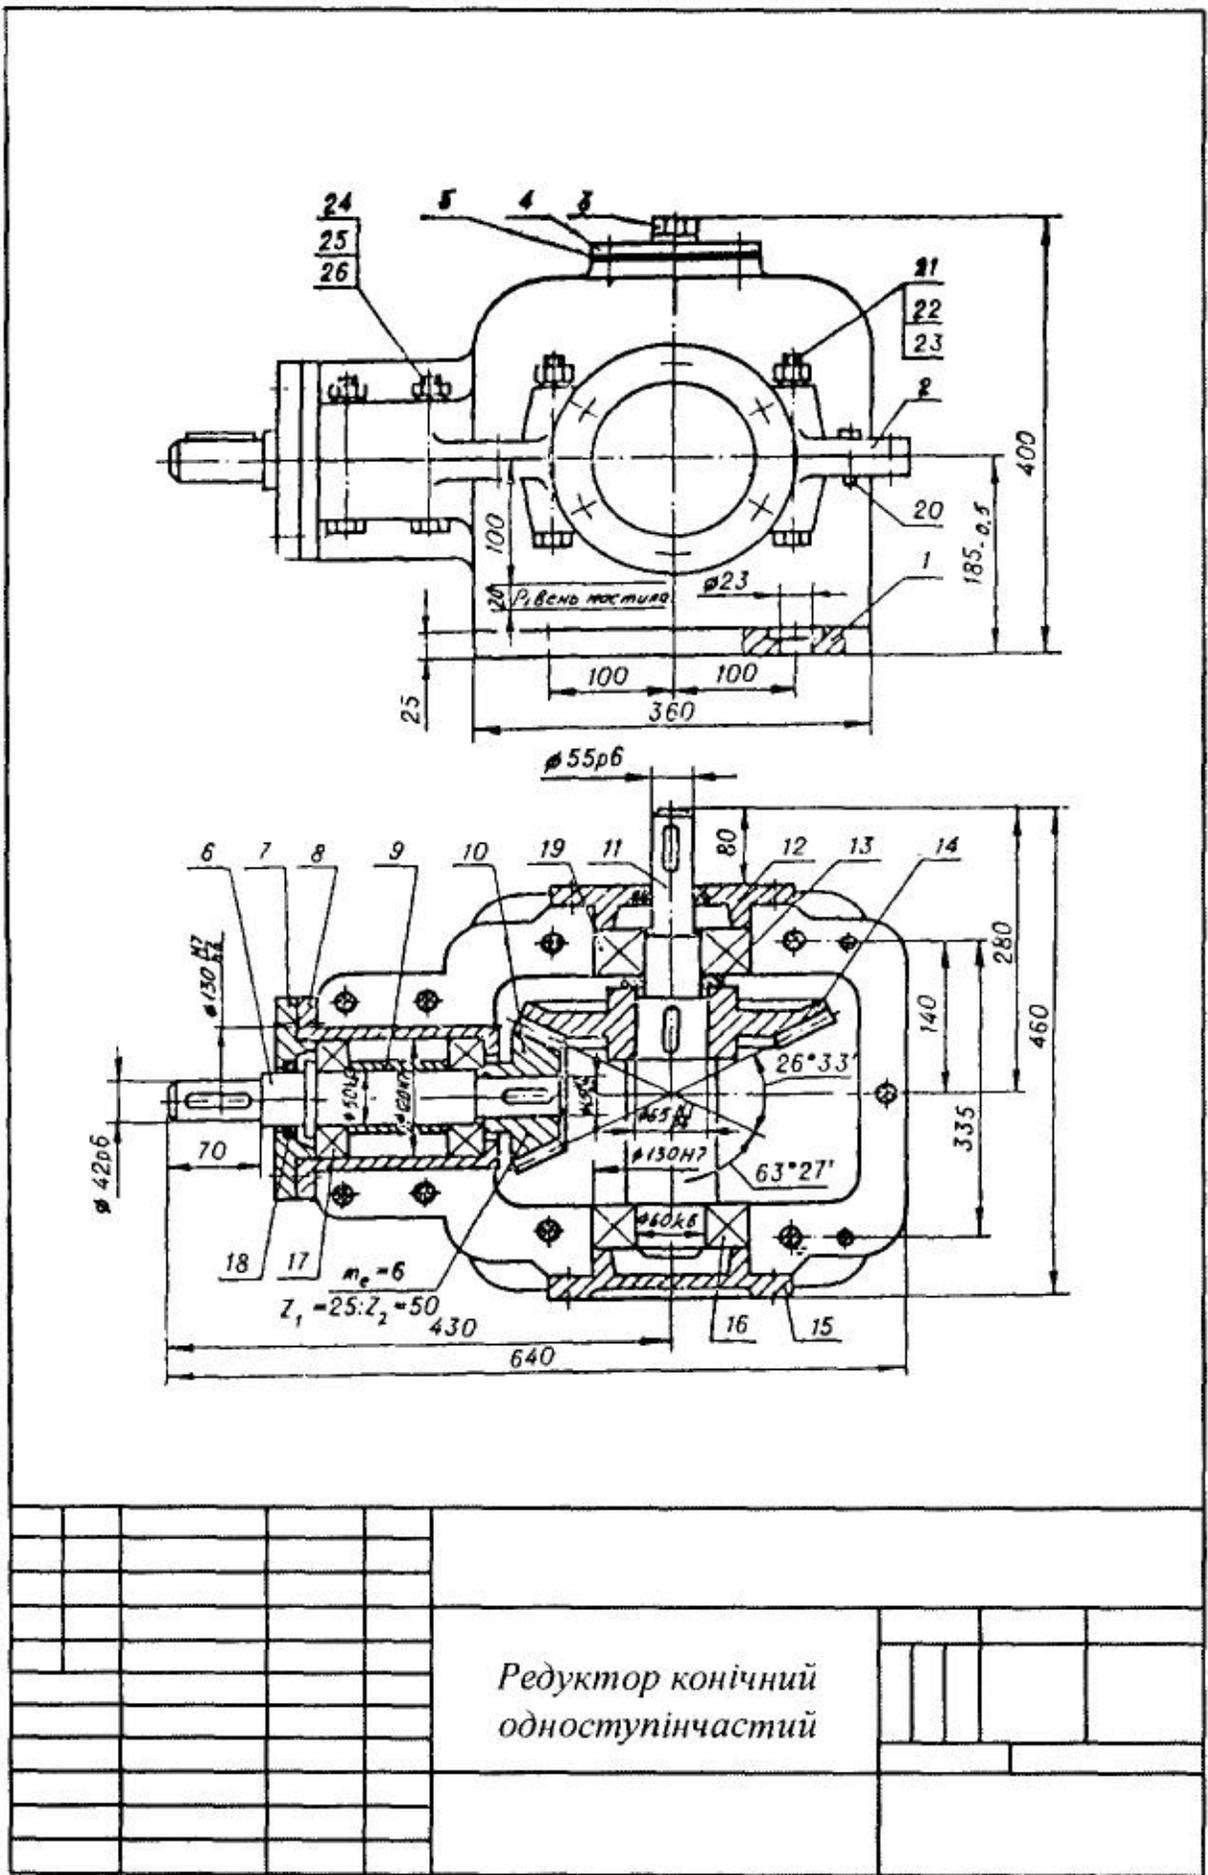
, а. Складальне креслення конічного одноступінчастого редуктора.
